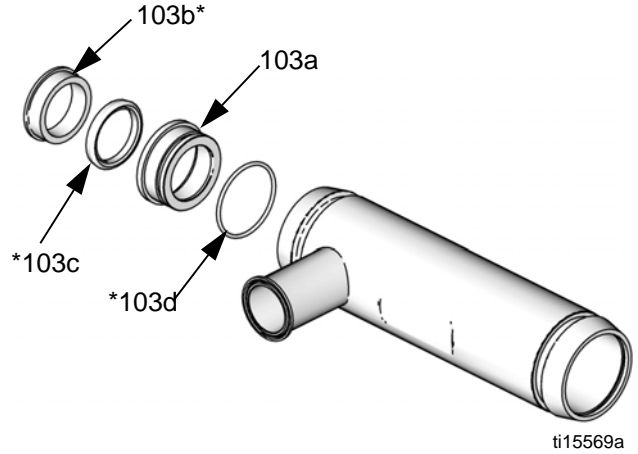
Retrait de l'ensemble de joint de la coupelle en U
